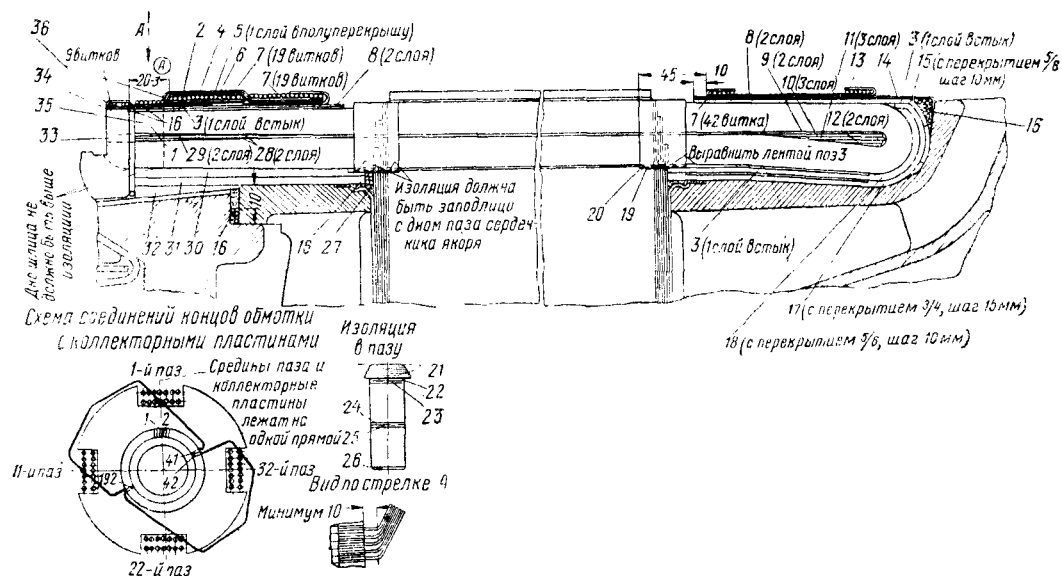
Катушка обмотки явора тягового двигателя типа GDTM-655
